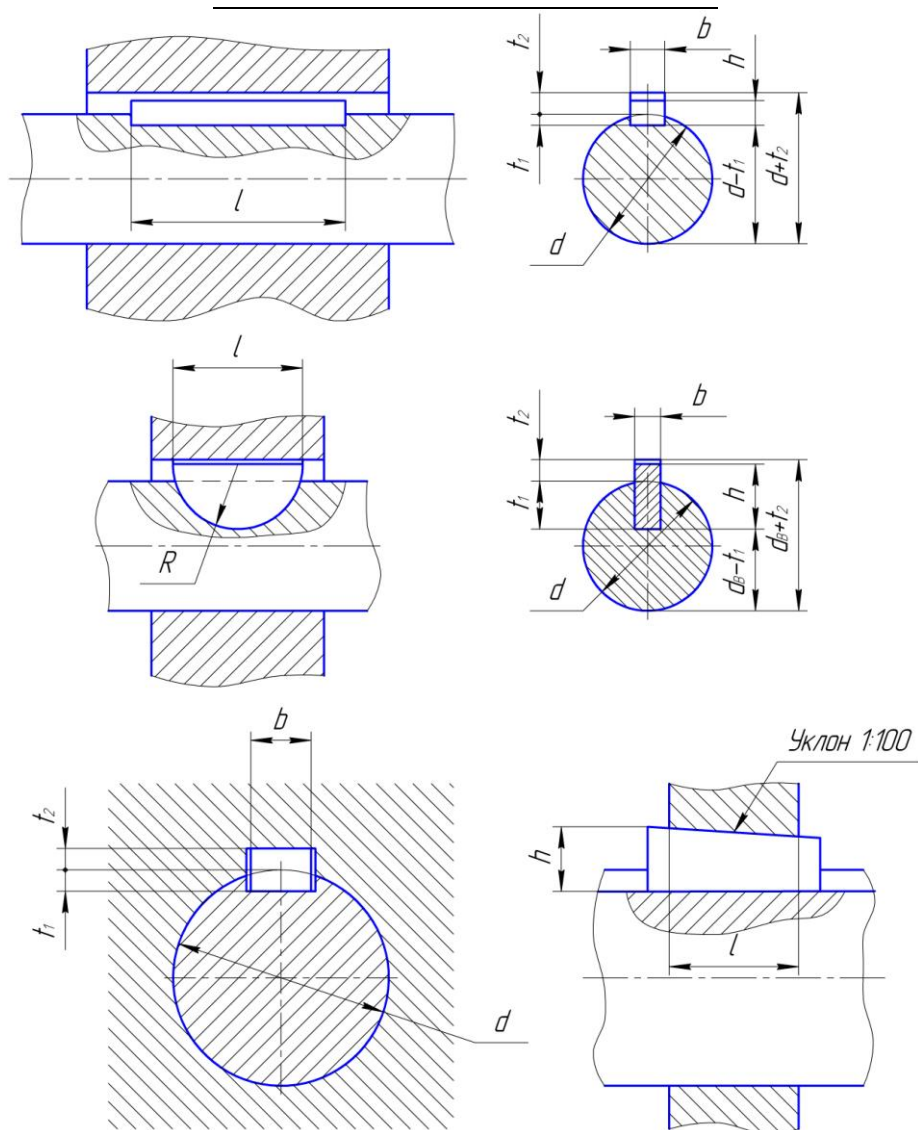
Шпонкове з'єднання маточин коліс з валами
